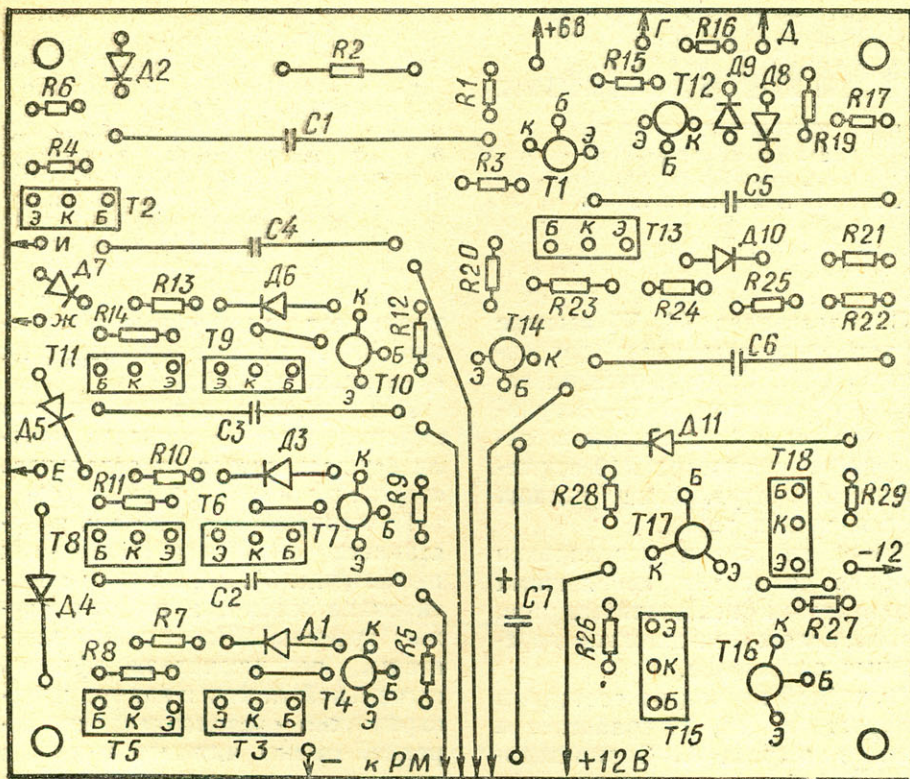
Печатная плата преобразователей и стабилизатора напряжения с расположением деталей.
